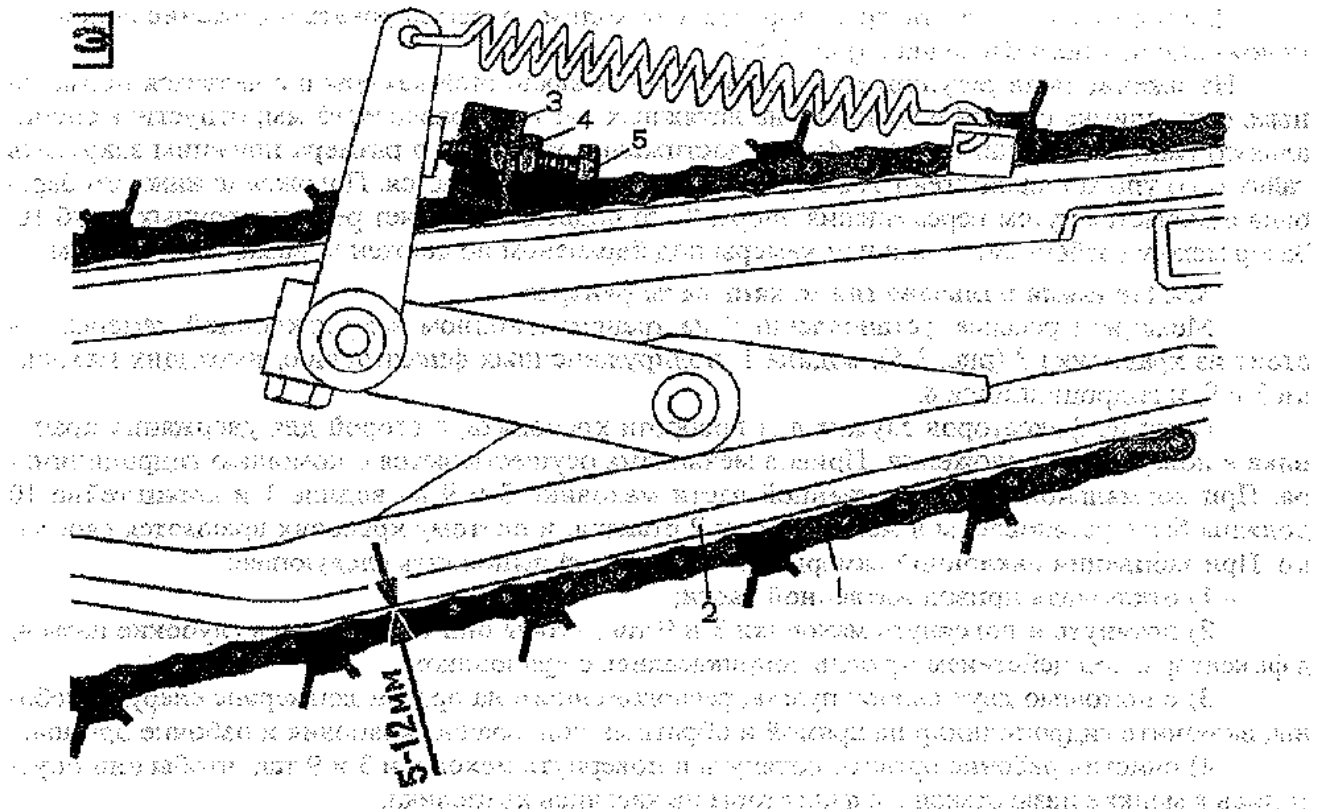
Схема регулировки положения ползьев: 1 – цепь; 2 – ползья; 3 – кронштейн; 4 – контргайка; 5 – болт
